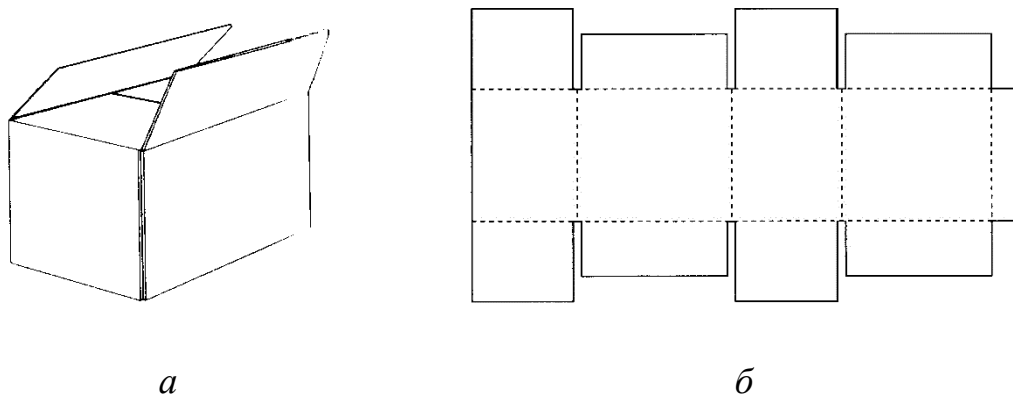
Внешний вид (а) и развертка (б) ящика с четырьмя клапанами
